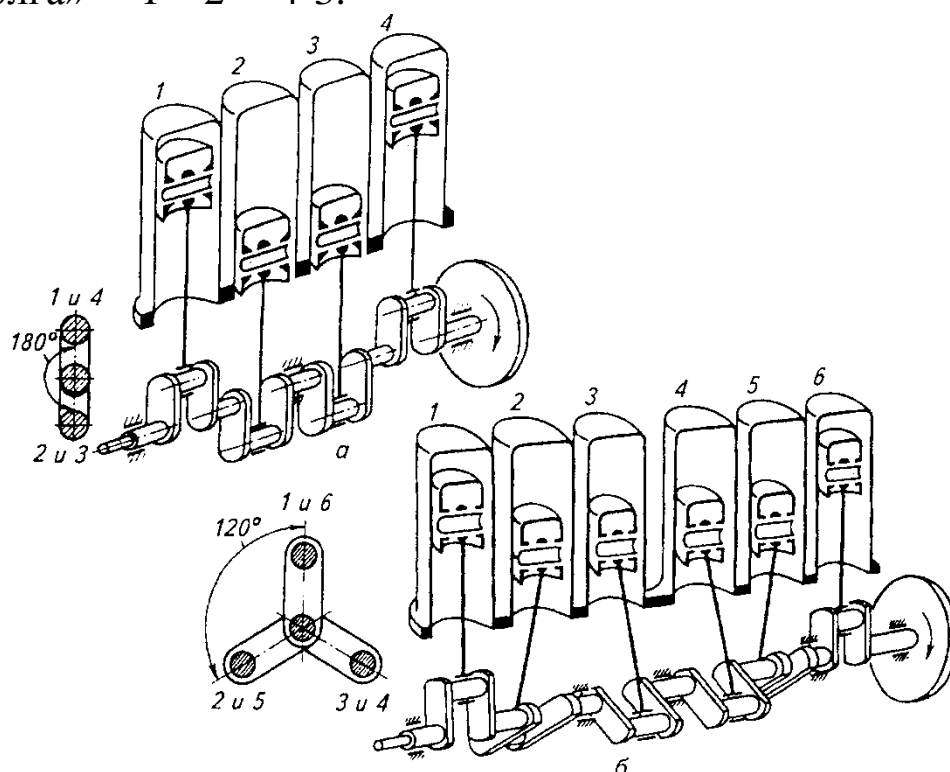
Схемы кривошипно-шатунных механизмов четырехтактных рядных двигателей: *a* — четырехцилиндрового; *б* — шестицилиндрового; 1...6 — цилиндры
